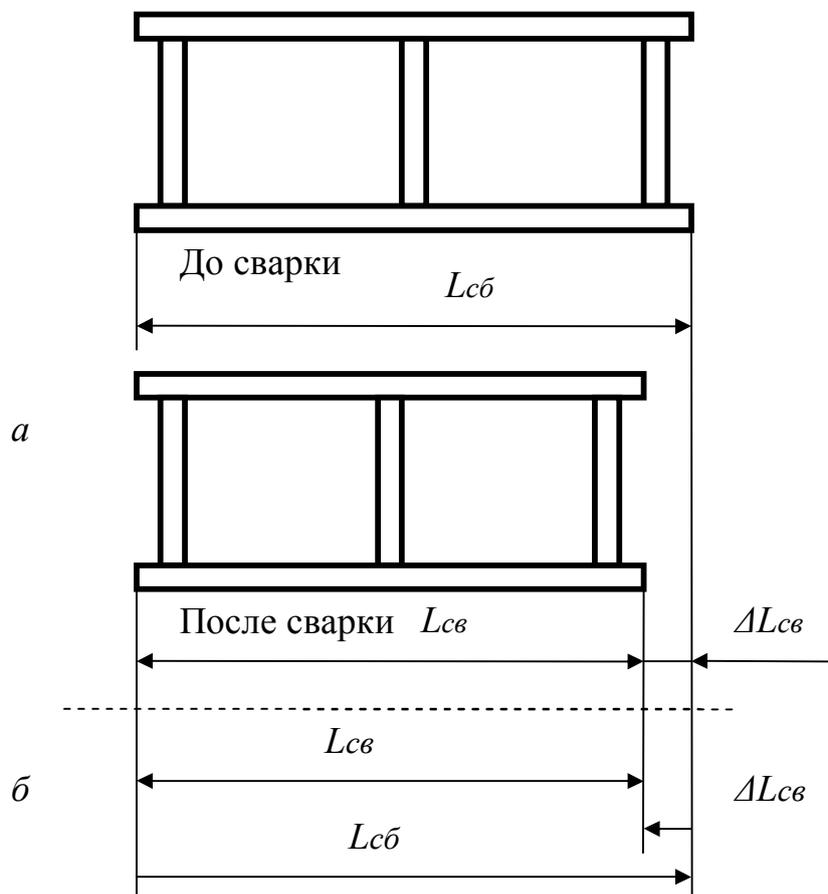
Схема введения суммарного сварочного укорочения в размерную цепь сварной конструкции:
